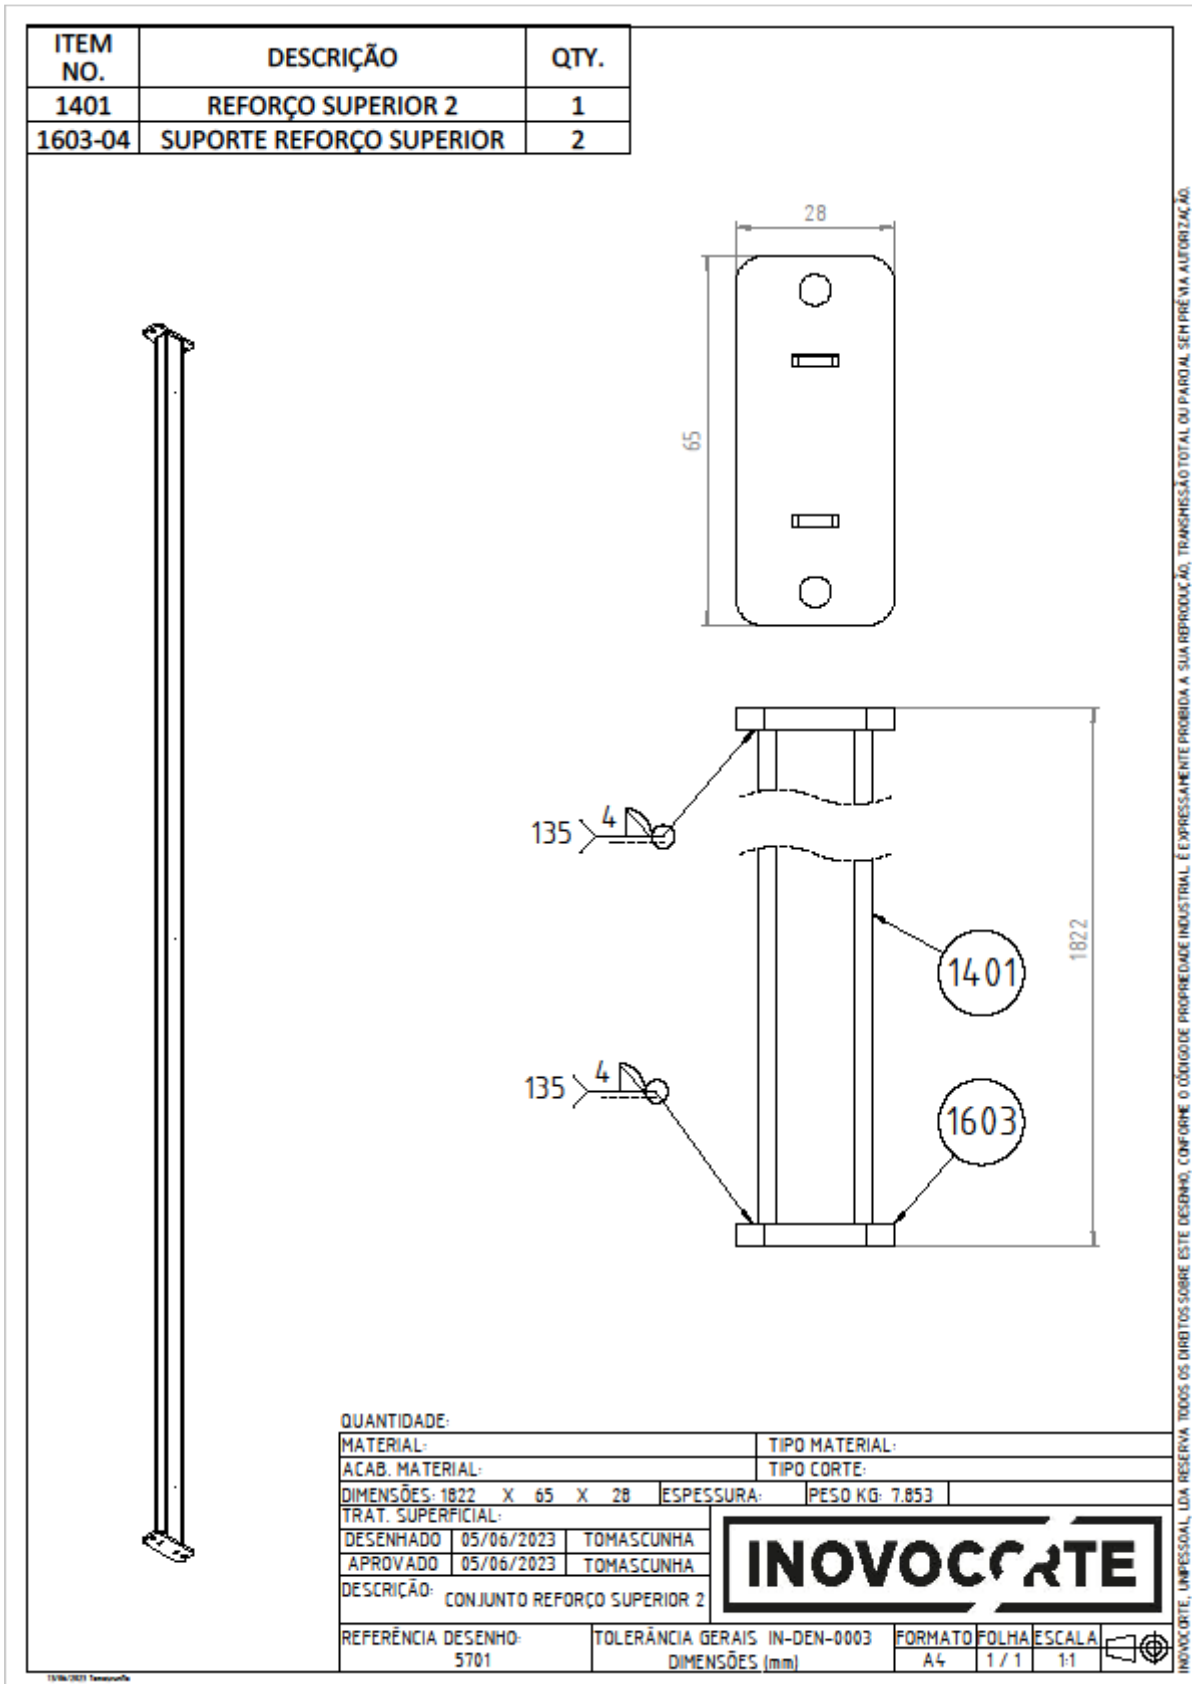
Desenho técnico do conjunto reforço superior 2 (5701).
